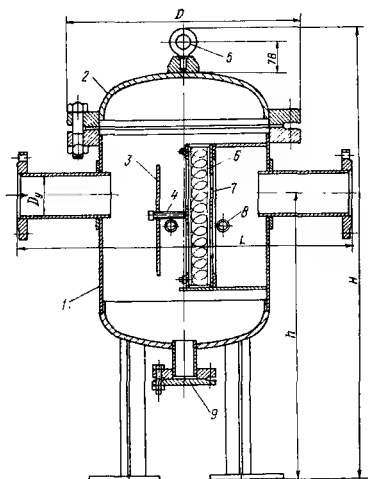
Фильтр кассетный сварной типа ФГ.
